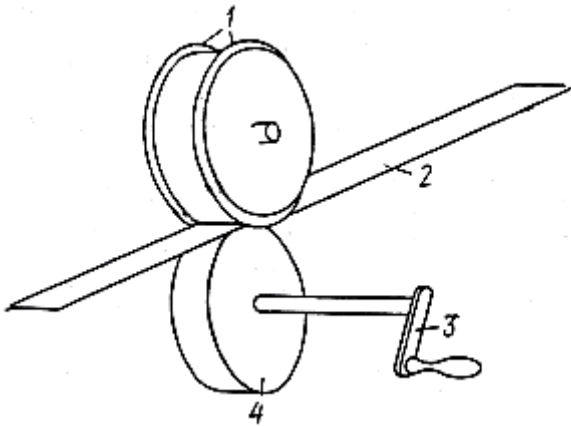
Пристосування для калібрування стрічки по ширині: 1- ріжучий ролик; 2 – калібрована стрічка; 3 – рукоятка; 4 – підтримуючий ролик.
